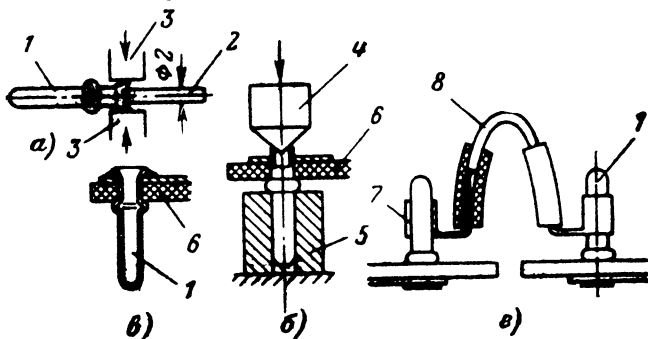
Установка ножки цоколя лампы с октальным цоколем на печатную плату.
